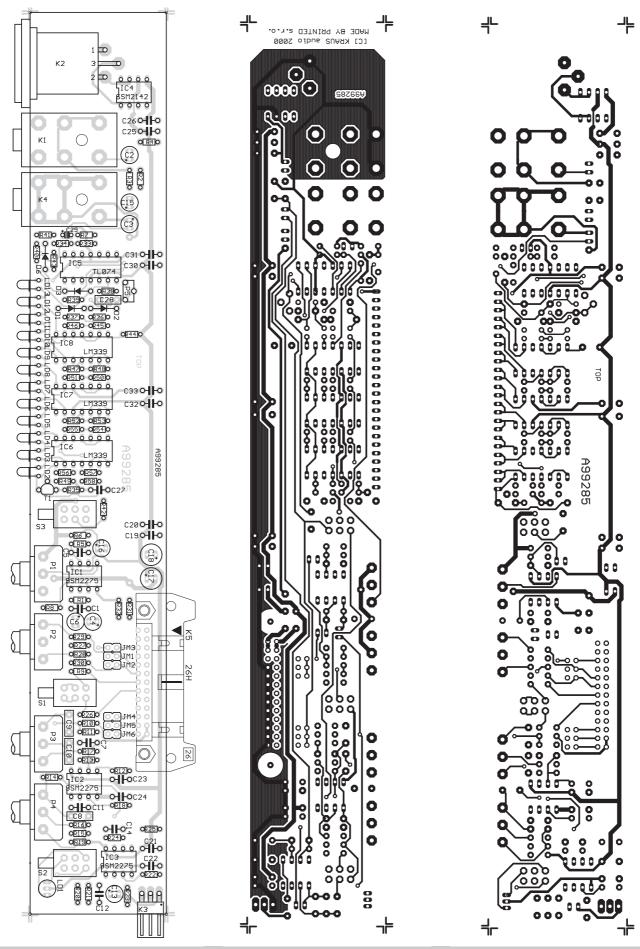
, 3 a 4. Rozložení součástek a obrazec desky s plošnými spoji vstupní jednotky. Skutečný rozměr je 265 x 40 mm
